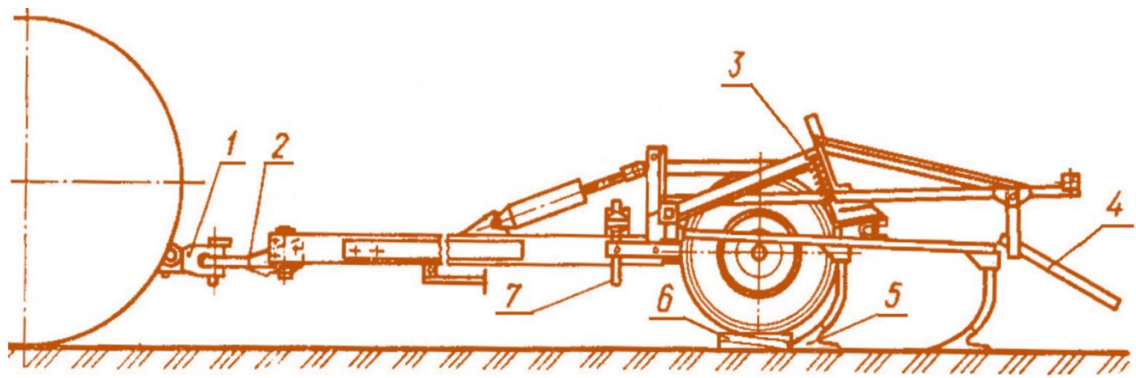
Схема встановлення культиватора на задану глибину обробітку: 1 - причіпна вилка трактора; 2 - причіпний кронштейн сниці; 3 – головка штанги; 4 - пристрій для навішування борін; 5 - стрілчаста лапа; 6 - набір підкладок; 7 - гвинтовий механізм регулювання глибини ходу робочих органів.
